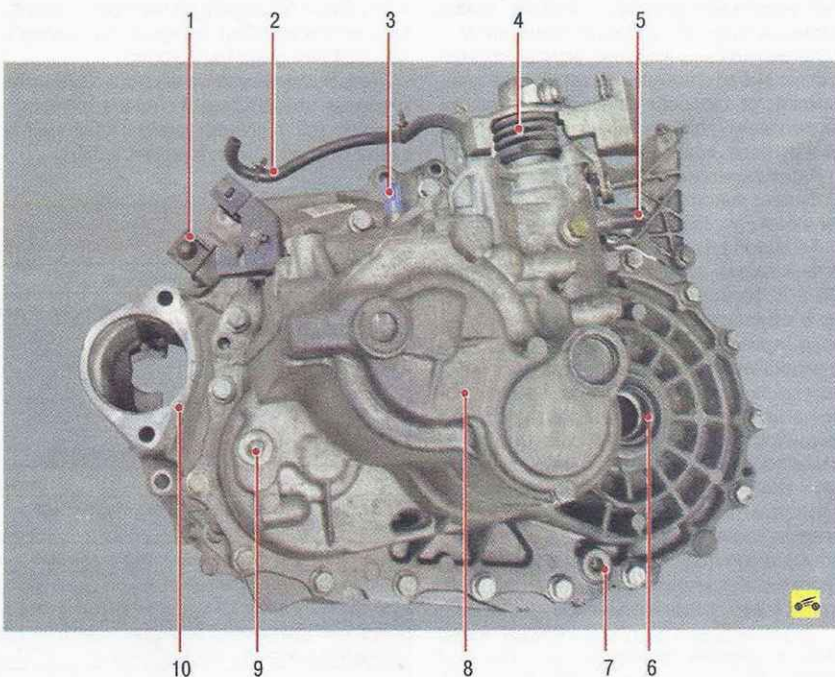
Шестиступенчатая механическая коробка передач RS6F51A: 1 – рычаг вилки выключения сцепления; 2 – шланг сапуна; 3 – датчик нейтрального положения передач; 4 – механизм выбора передач; 5 – выключатель света заднего хода; 6 – сальник полуоси; 7 – пробка сливного отверстия; 8 – картер коробки передач; 9 – пробка наливного отверстия; 10 – картер сцепления с отверстием для установки стартера
